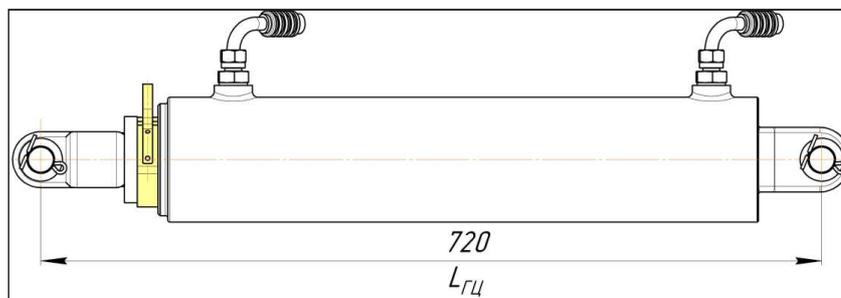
Гидроцилиндр МС100/50х400-20.404А.ОАОА.720.01.Г(052)
